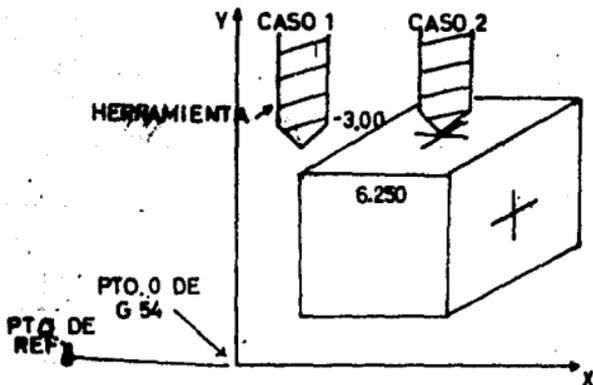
EJEMPLO DE BARRENADO USANDO LAS COORDENADAS G54
